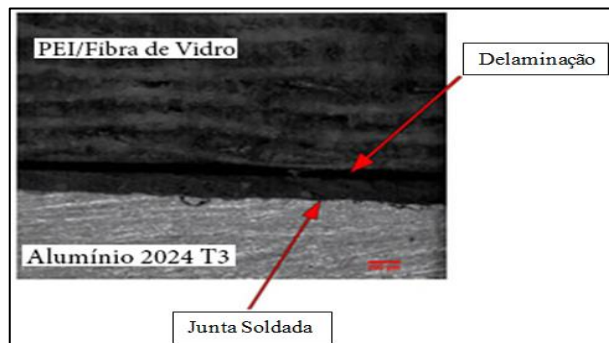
Amostra de PEI/Vidro e Alumínio 2024 T3 soldados com escala de 4,5x. Observa-se a ocorrência de delaminação na junta já soldada.
